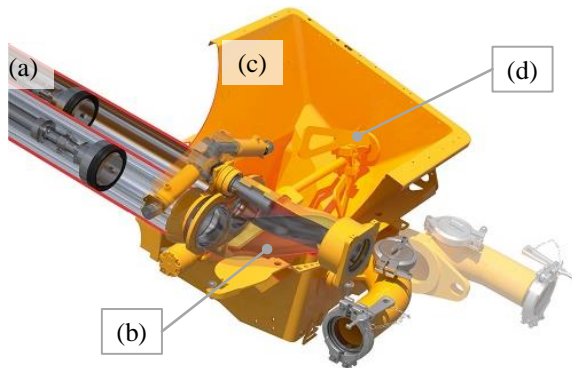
Kolbenpumpe mit Schwenkrohrventil (Schnittansicht); Beschriftung: (a) Förderkolben, (b) Schwenkrohrventil (hier S-Rohr), (c) Trichter, (d) Rührwerk [42]
